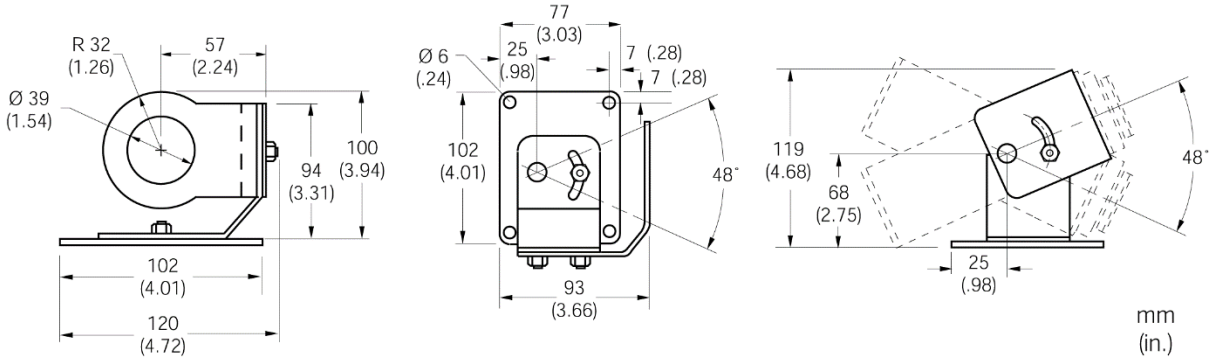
Equerre de montage ajustable (XXXTXXACAB)
